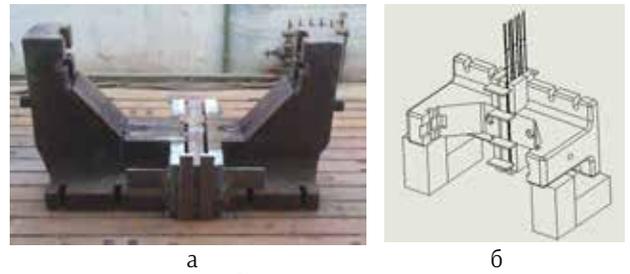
Ремонт корпуса бойка к прессу усилием 5000 тс со сложной, разветвленной трещиной: а – корпус бойка, после разделки трещины механической обработкой, собранный с центральной вставкой под ЭШС, б – положение детали при ЭШС
